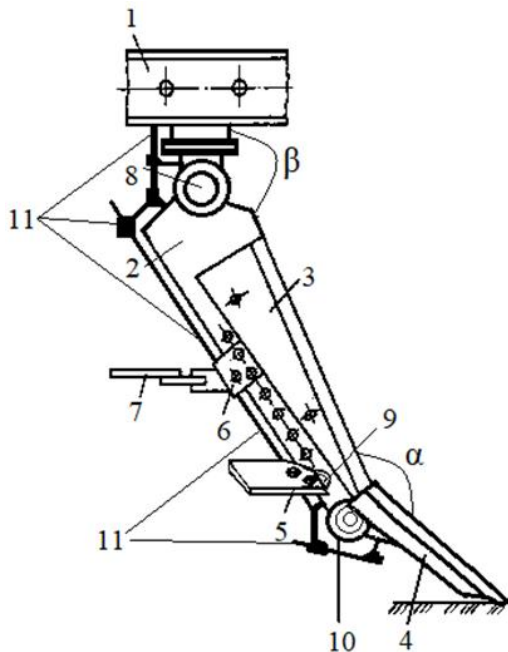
Схема рабочего органа адаптивного глубокорыхлителя – вид сбоку
